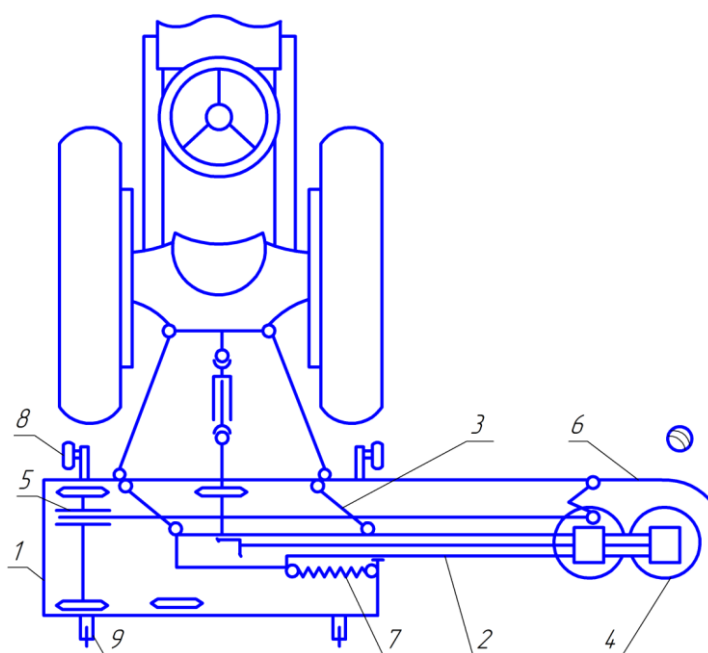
Схема двухроторной фрезы с механическим приводом исполнительного механизма
